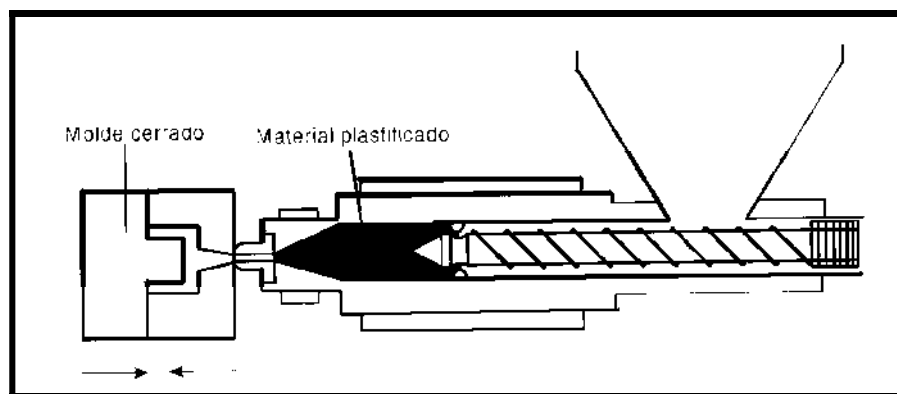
Cierre del molde y comienzo de la inyección.
